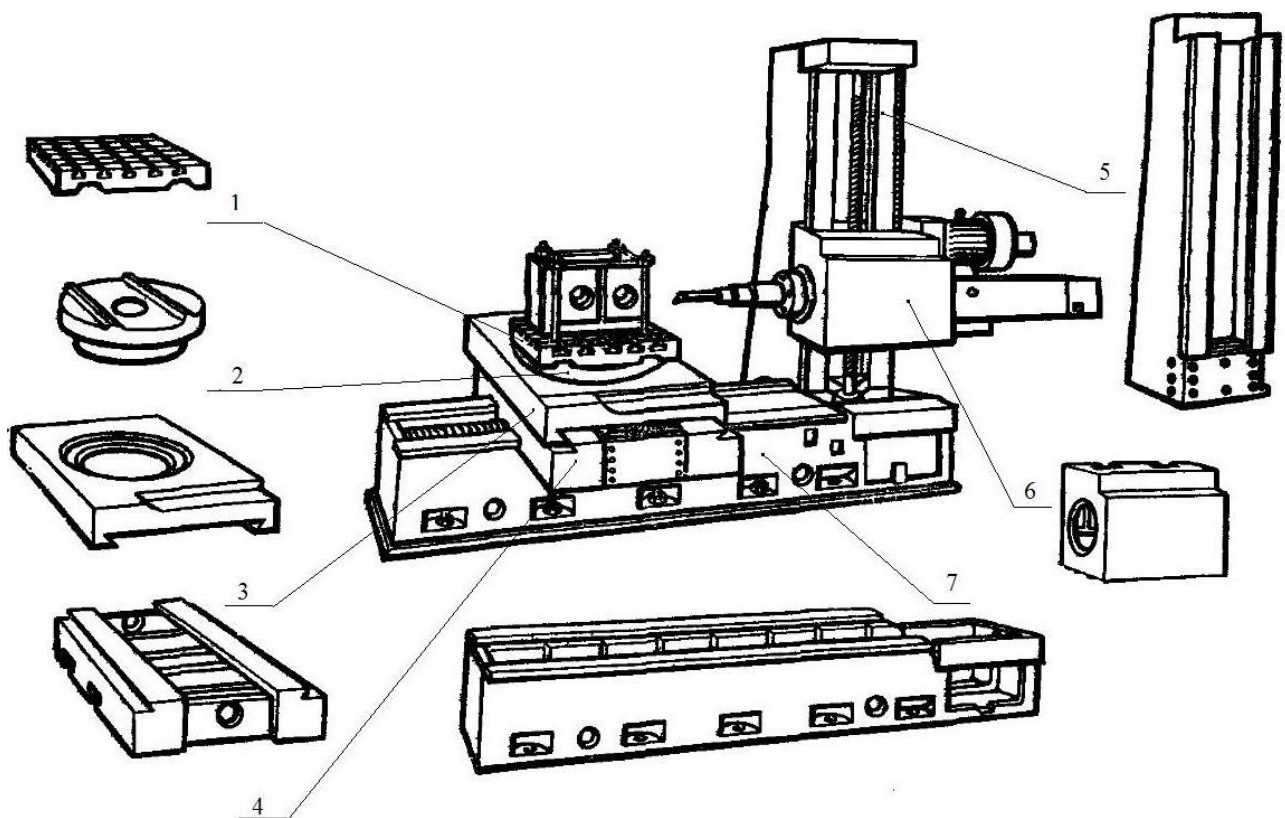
Базові деталі фрезерно-розточувального верстата:
